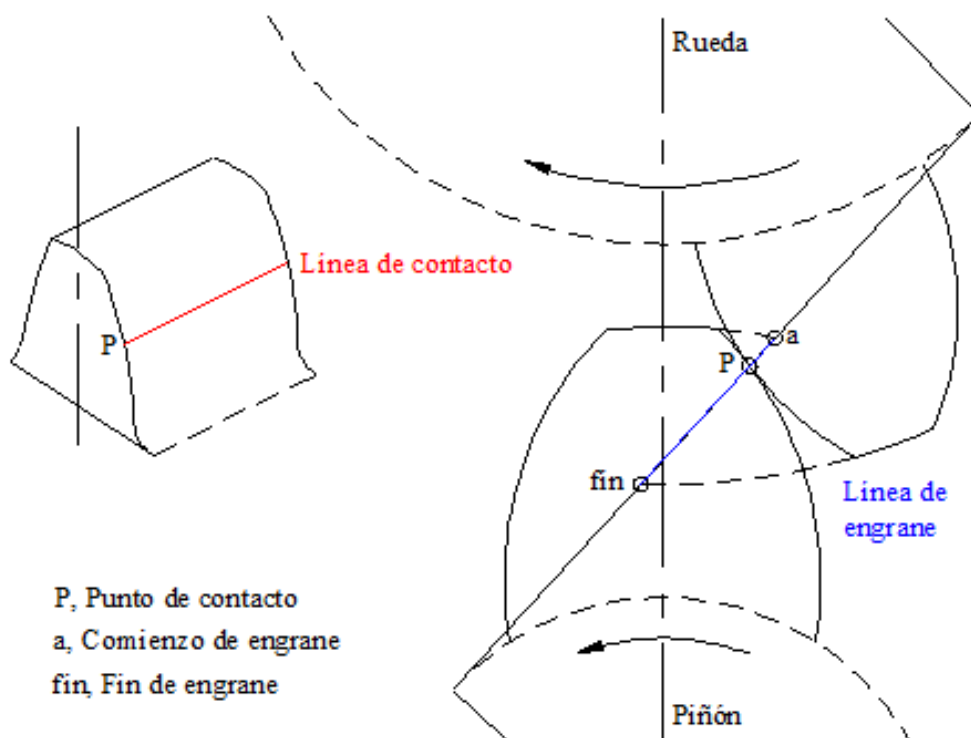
Engrane en una transmisión de engranajes cilíndricos de dientes rectos.
